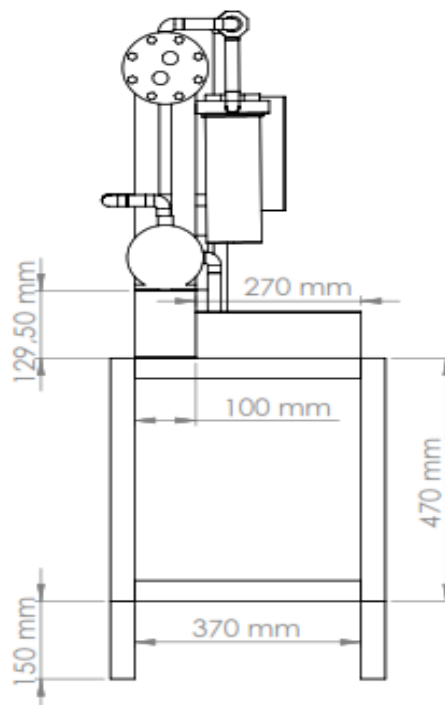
Technical Drawing Assembly Prototipe Tampak Depan
